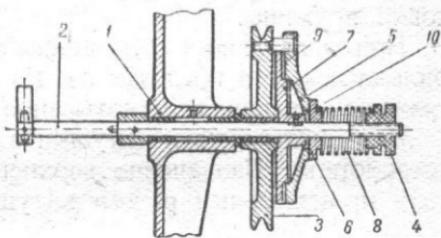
Фрикцион нижней катушки в разрезе: 1—кронштейн; 2—вал; 3—шкив с пальцами; 4—гайка; 5—муфта; 6, 7—фланцы; 8—пружина; 9—шайба; 10—винт
